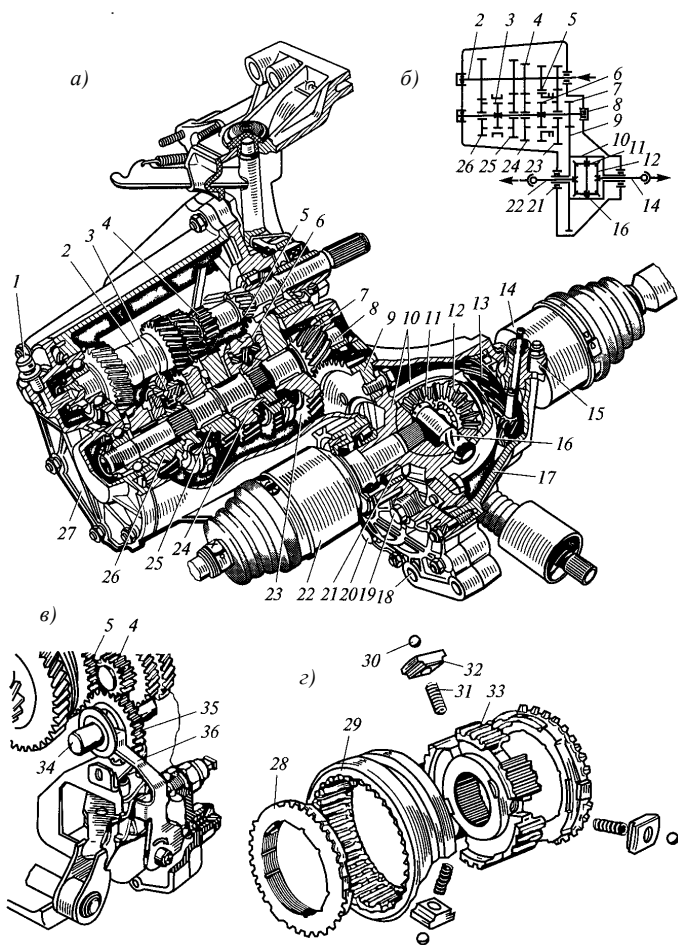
Коробка передач переднеприводных легковых автомобилей ВАЗ:
